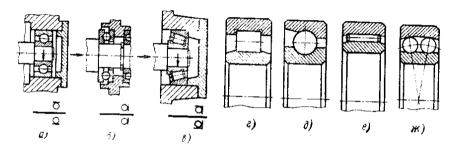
Виды подшипников качения: а – радиальный; б – упорный; в – радиально-упорный; г – роликовый; д – шариковый радиально-упорный; е – игольчатый; ж – шариковый двухрядный самоустанавливающийся
